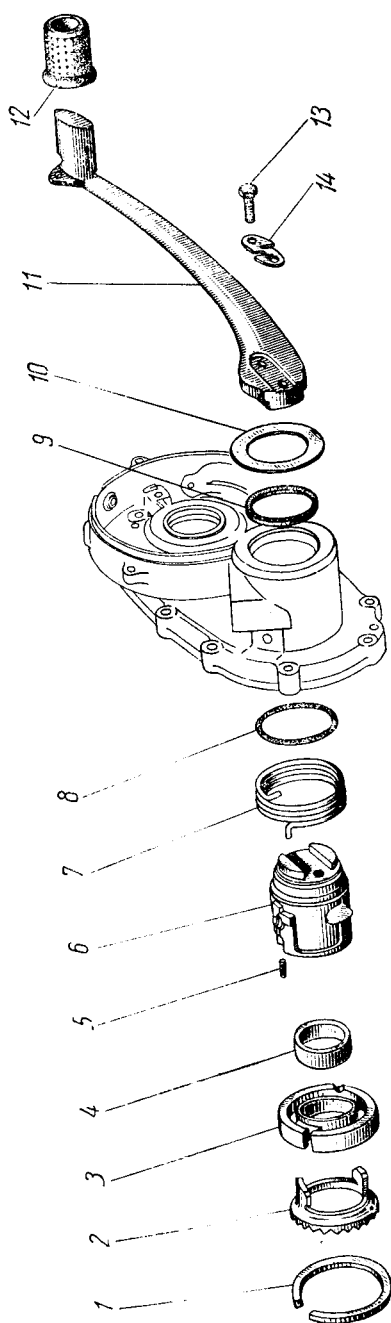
Пусковой механизм коробки передач мотороллеров ВП-150 и В-150М:
